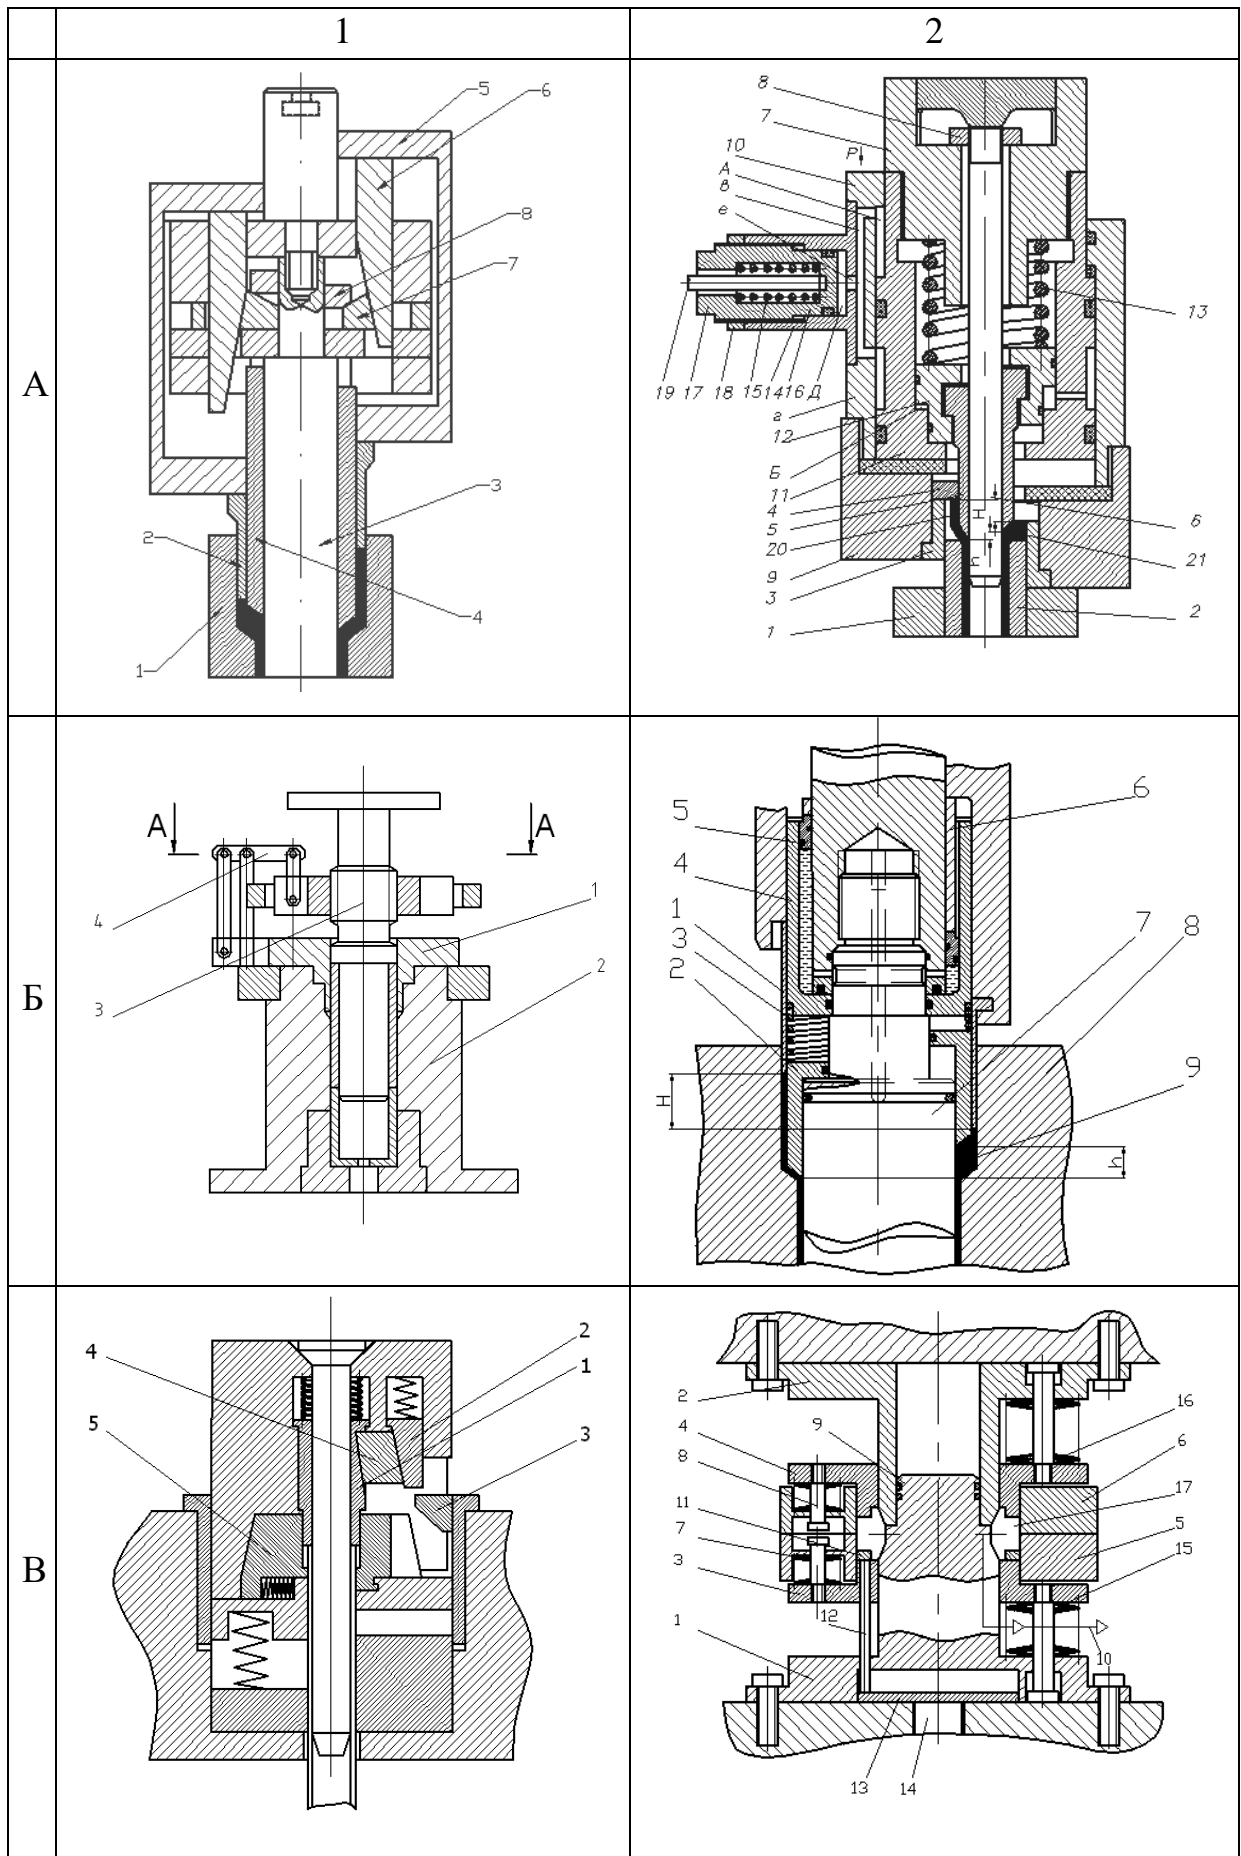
Конструкции штампов с подвижными полуматрицами
